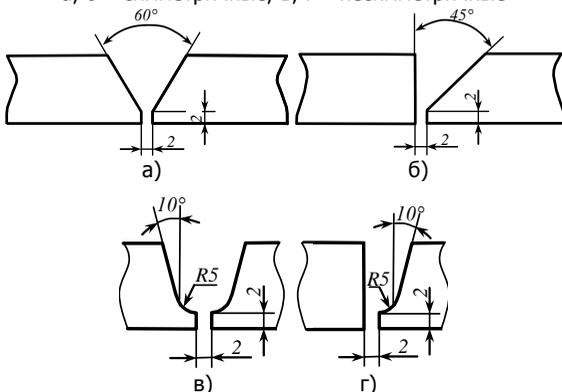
Односторонние разделки кромок под сварку:
